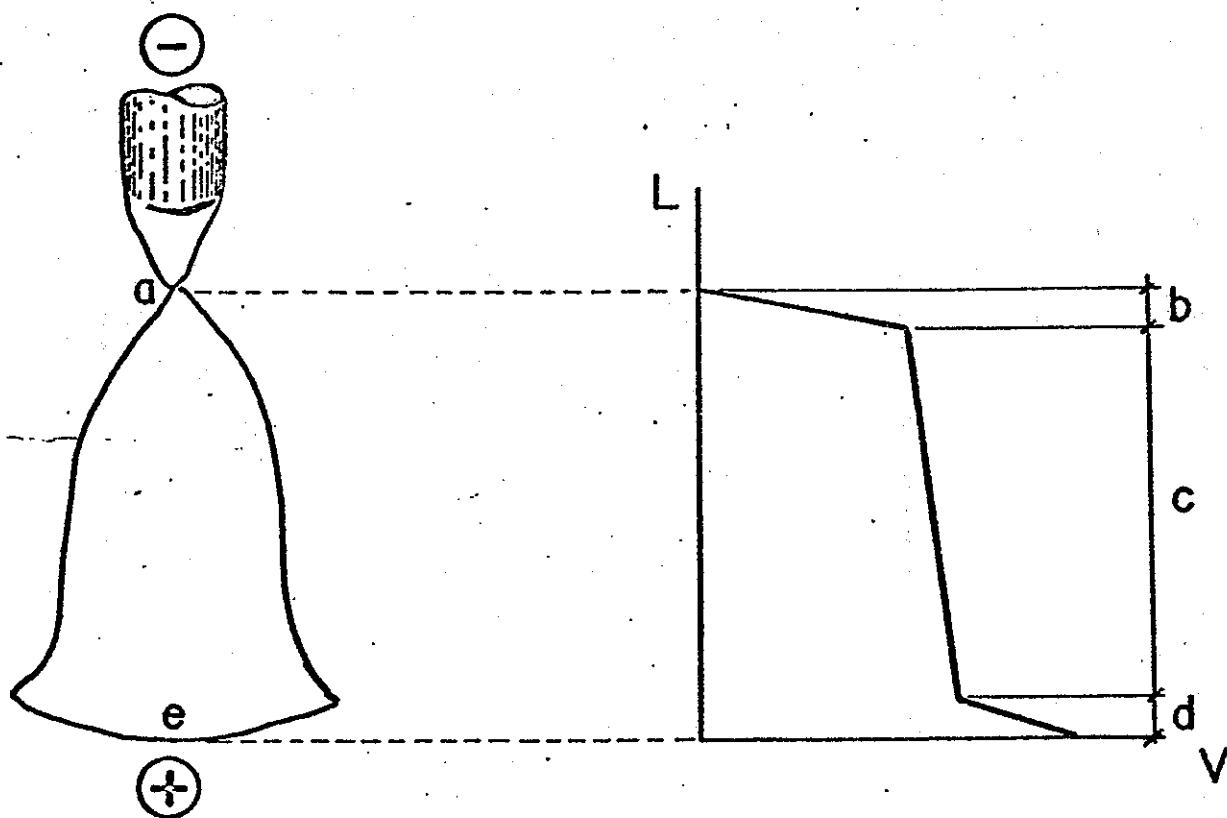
Representação esquemática do Arco Elétrico em Soldagem.
